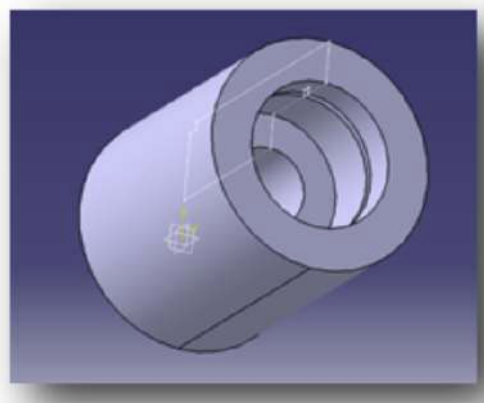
Primera pieza del molde. Fuente: Elaboración propia
